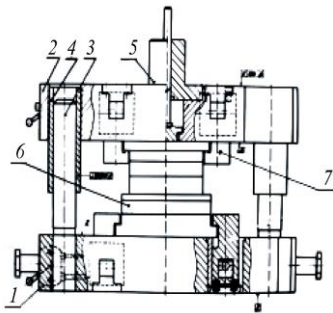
Конструкция перенастраиваемого штампа с механизированными прихватами:
